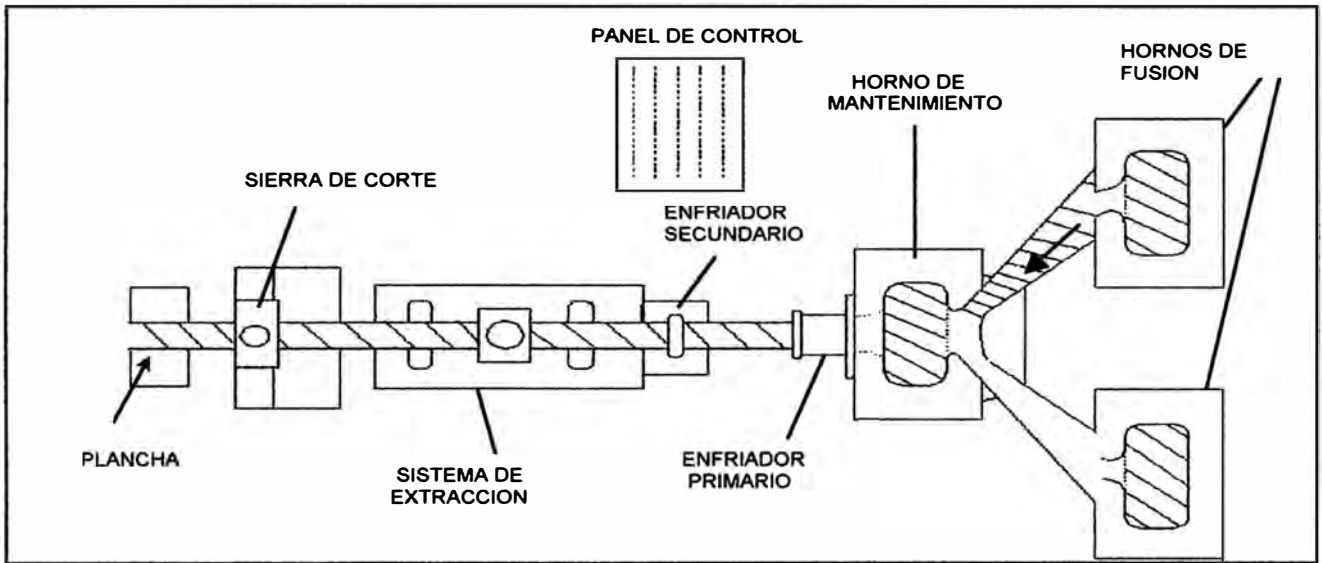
VISTA DE PLANTA DEL SISTEMA DE COLADA CONTINUA
